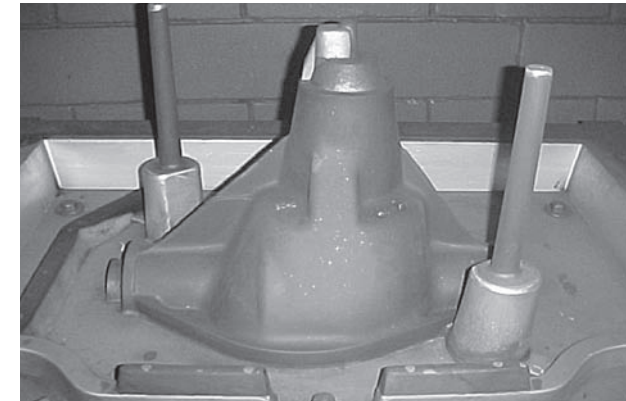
Herramental con una figura de carcasa de diferencial mod.80
